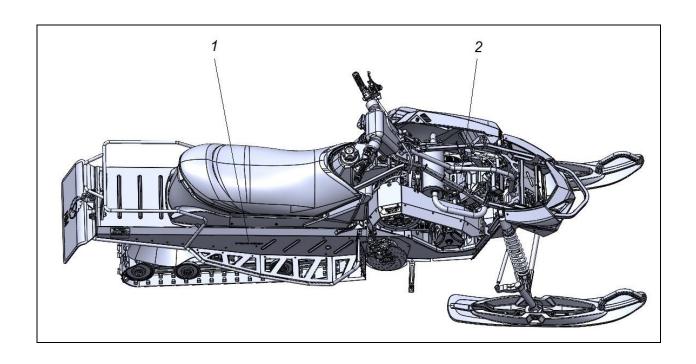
Расположение номера снегохода и двигателя 1 — номер снегохода; 2- номер двигателя.
